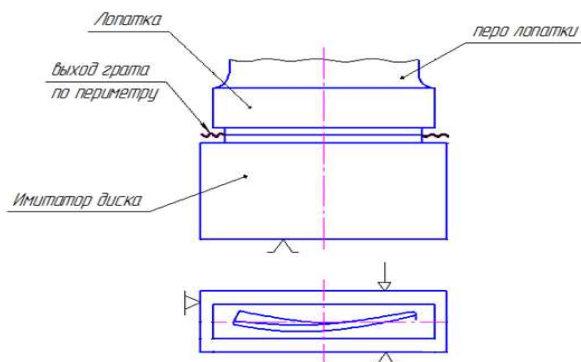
Схема базирования заготовки образца на станке МТЕ 500V/5
